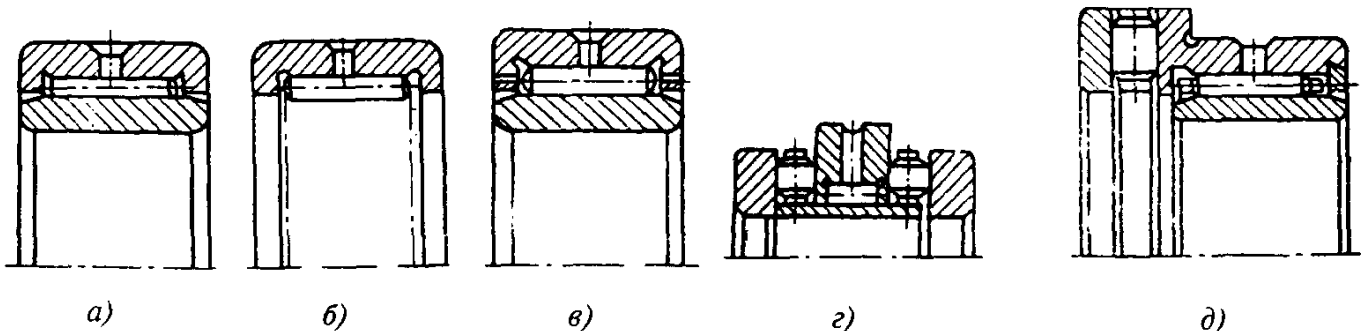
Подшипники радиальные роликовые игольчатые или роликовые с длинными цилиндрическими роликами исполнений:
